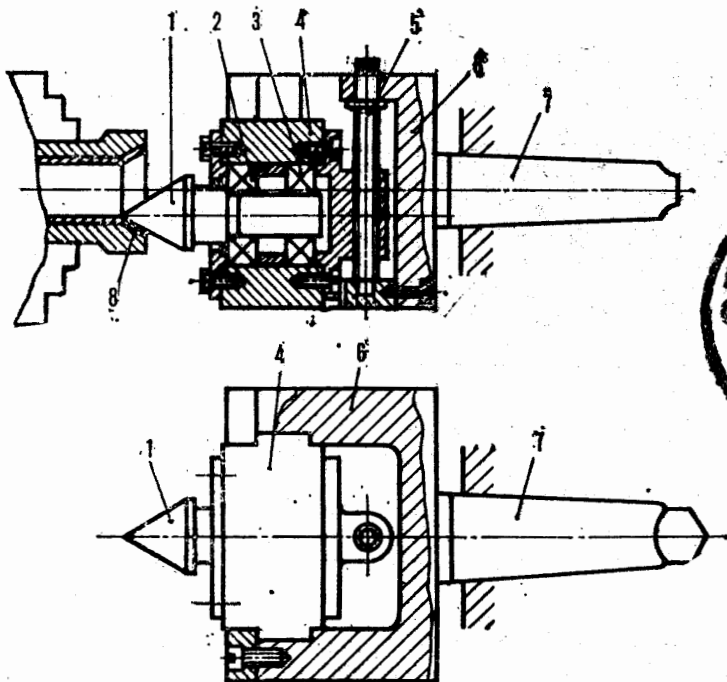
Схема развальцовки: 1 — конусный ролик, 2 — конический роликоподшипник, 3 — радиально-упорный шарикоподшипник, 4 — ползун, 5 — винт для смещения ползуна, 6 — корпус, 7 — хвостовик, 8 — труба.
